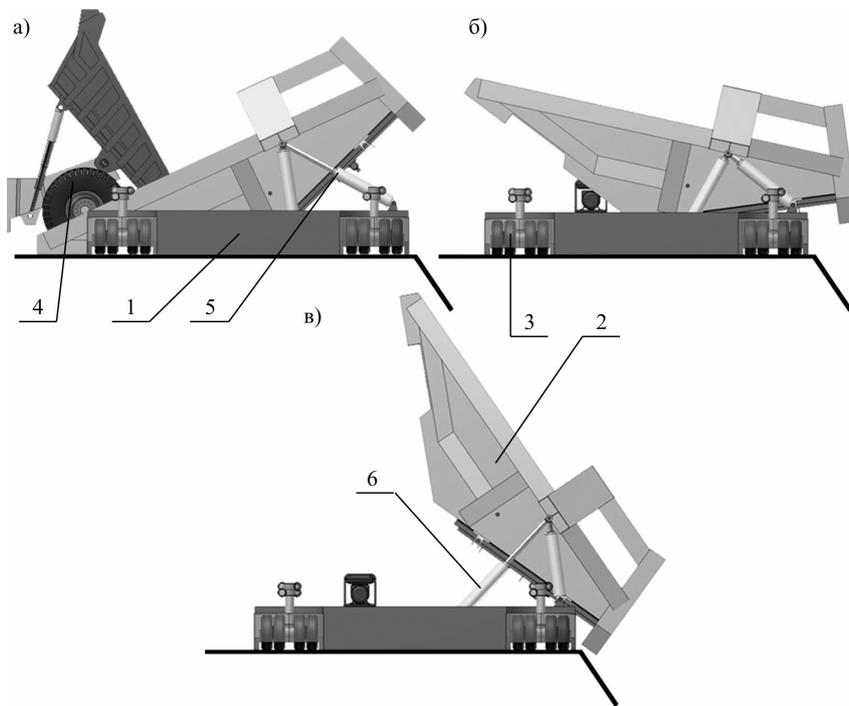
Схема работы вибрационного отвалообразователя: а — разгрузка самосвала; б — поворот рабочего органа отвалообразователя; в — разгрузка отвалообразователя; 1 — опорная рама; 2 — рабочий орган; 3 — механизм передвижения; 4 — автосамосвал; 5, 6 — гидроцилиндры
